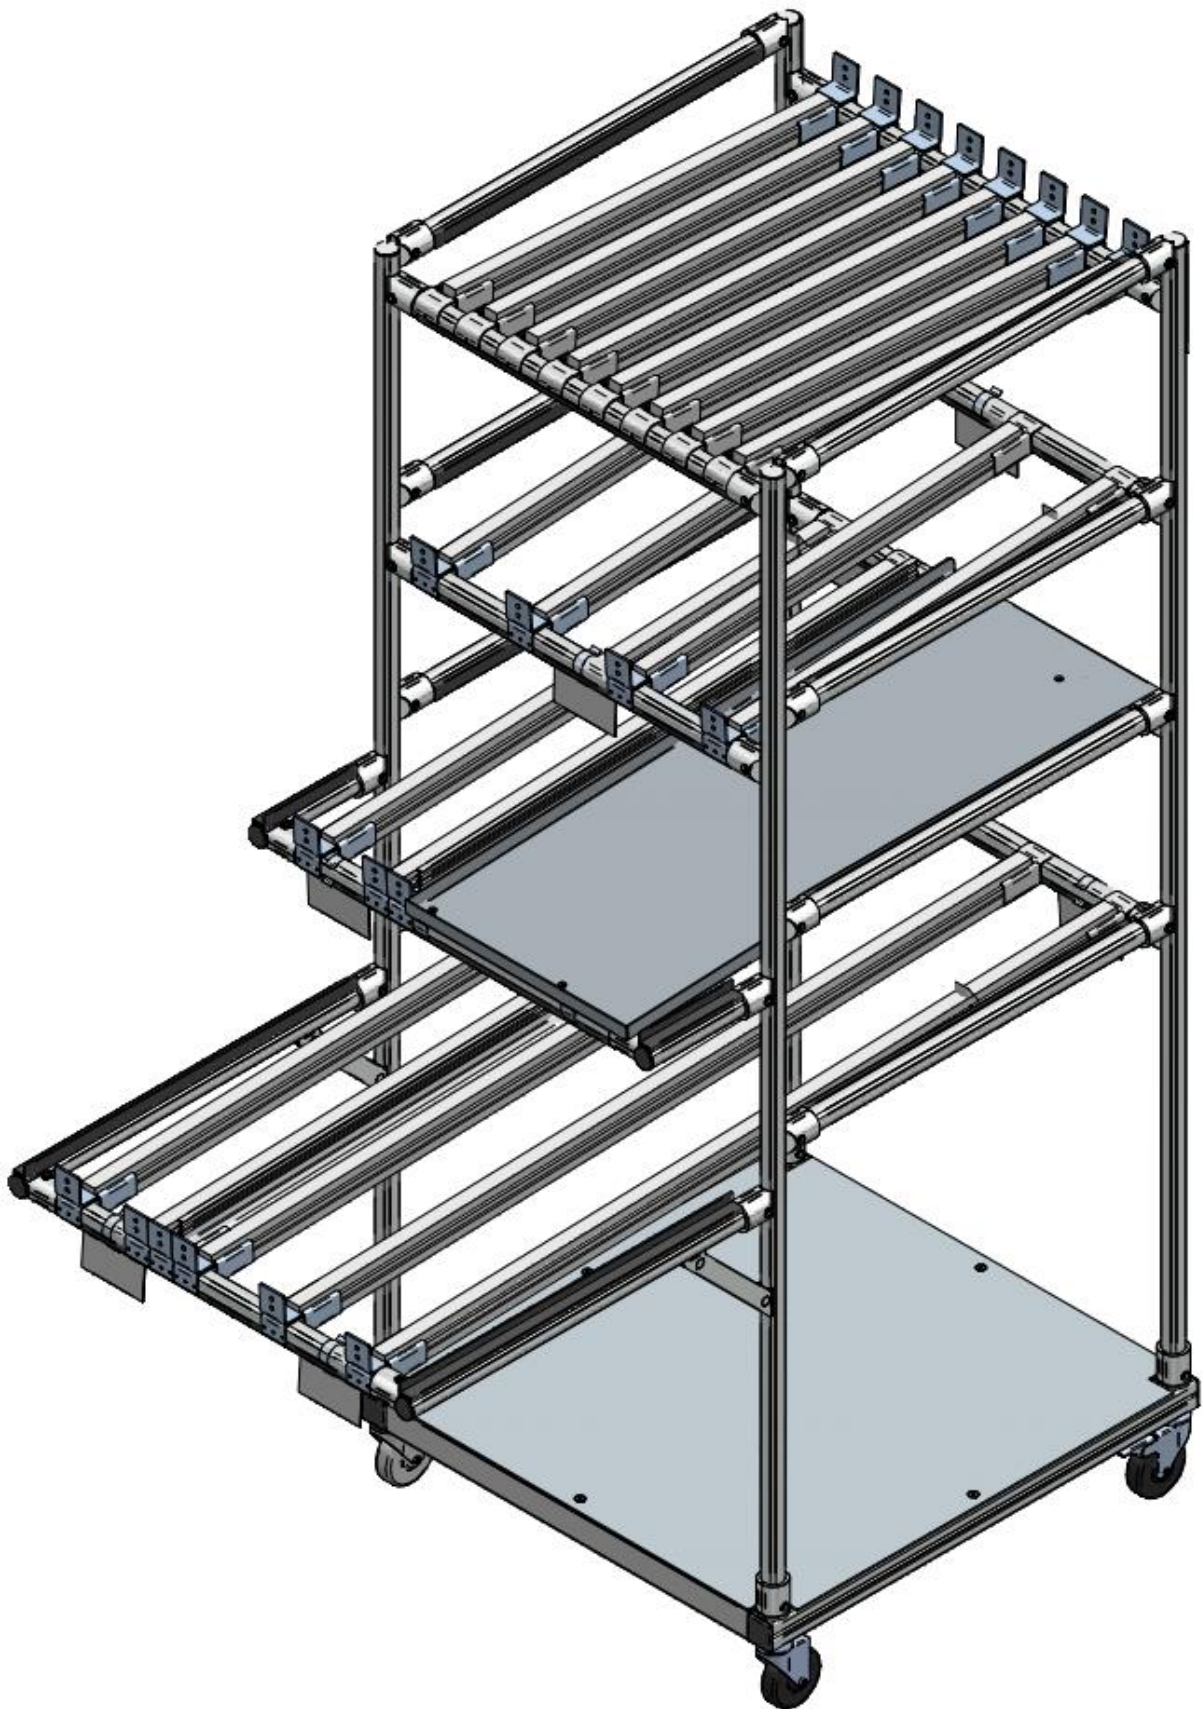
BOL para o equipamento OP10 Rear – lado esquerdo
